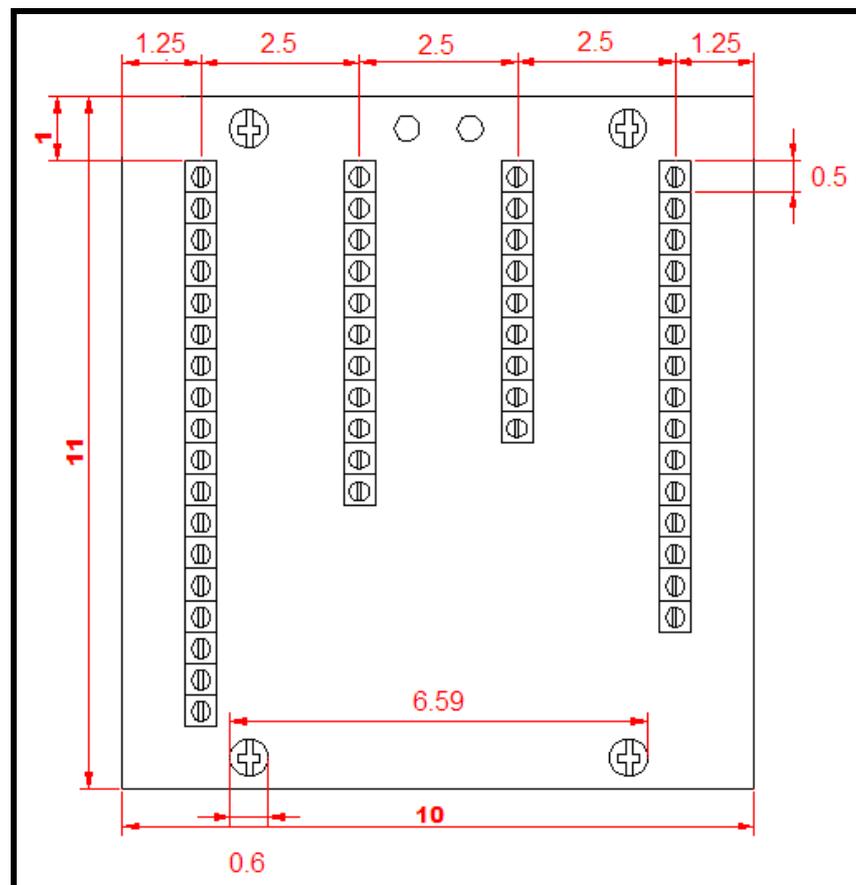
34. Dimensiones del Módulo de I/O del Puerto GPIO (Dimensiones en cm.)
